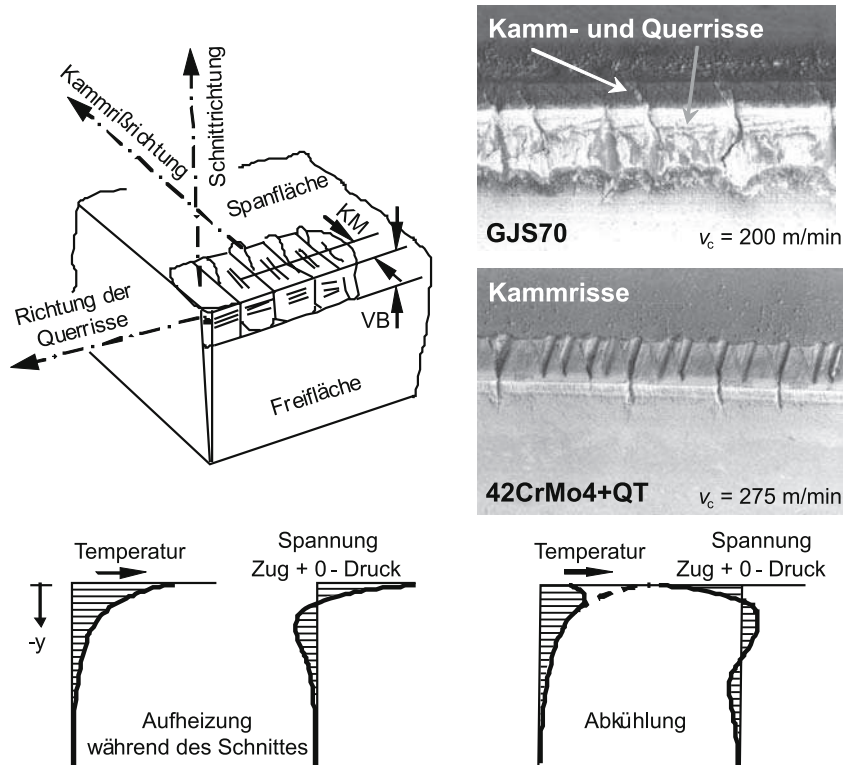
Kamm- und Querrissbildung beim Fräsen, nach Vieregge [Vier59]
